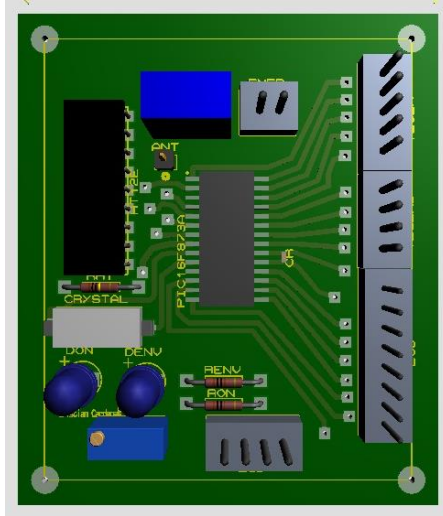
Vista 3D Proteus módulo Cuerpo Técnico
